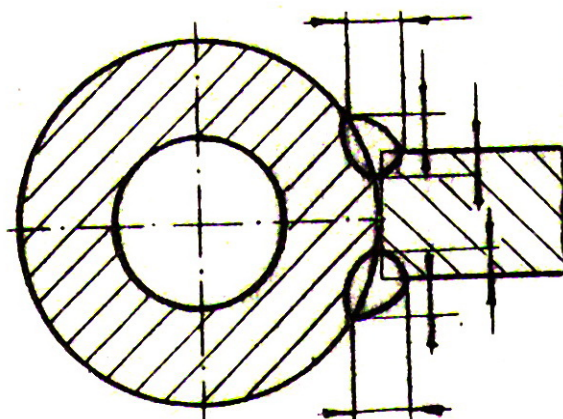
Изображение нестандартных швов сварных соединений
